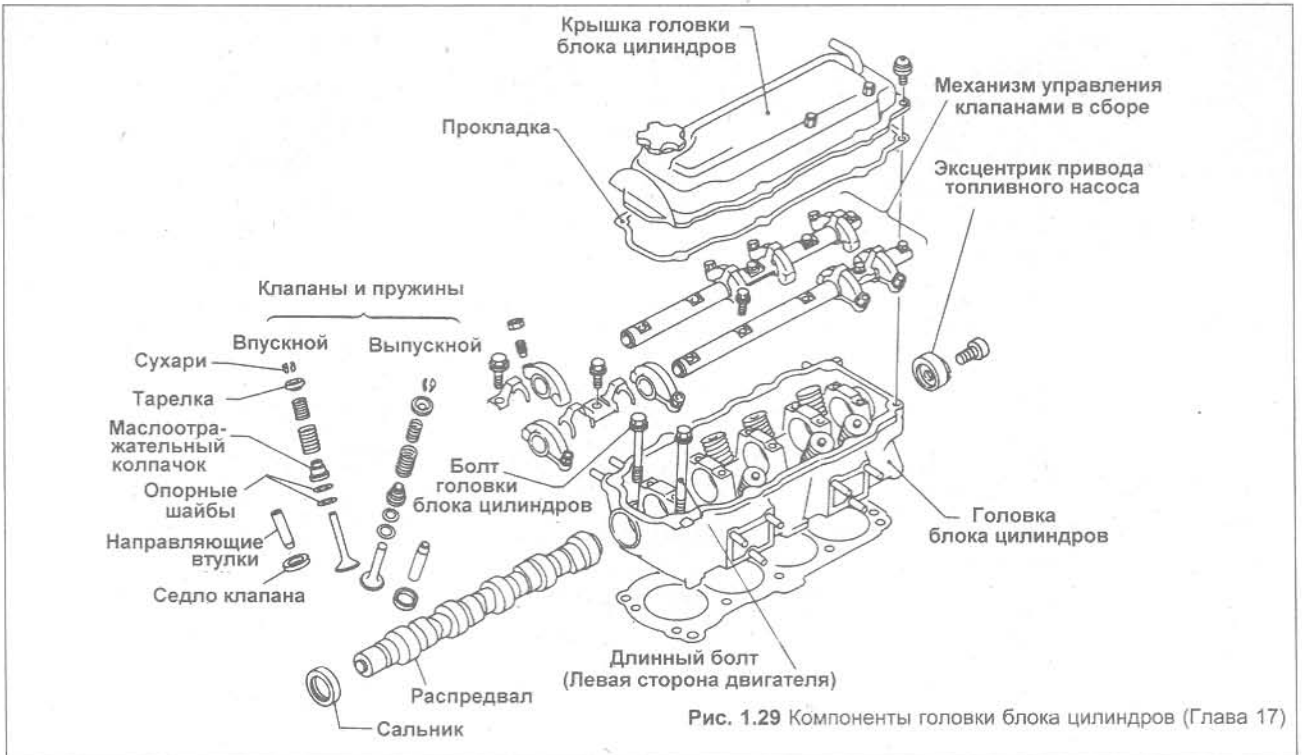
Компоненты головки блока цилиндров (Глава 17)
